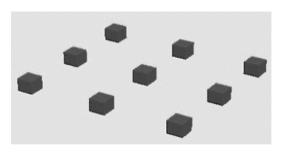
托盘底柱示意 Fig.1 Pillar arrangement of the pallet
